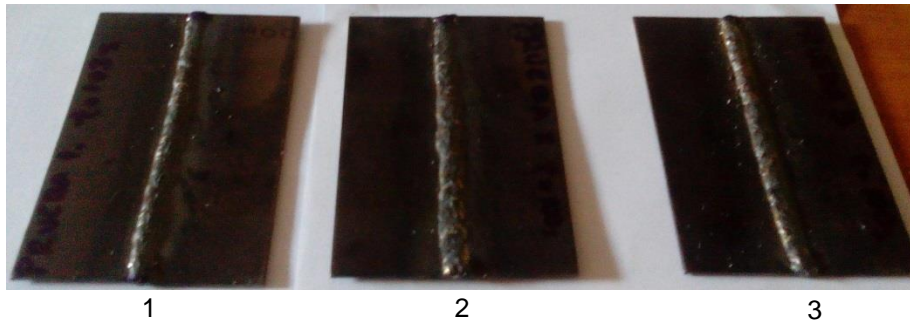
Juntas soldadas con placas de 50.8 mm de ancho.
